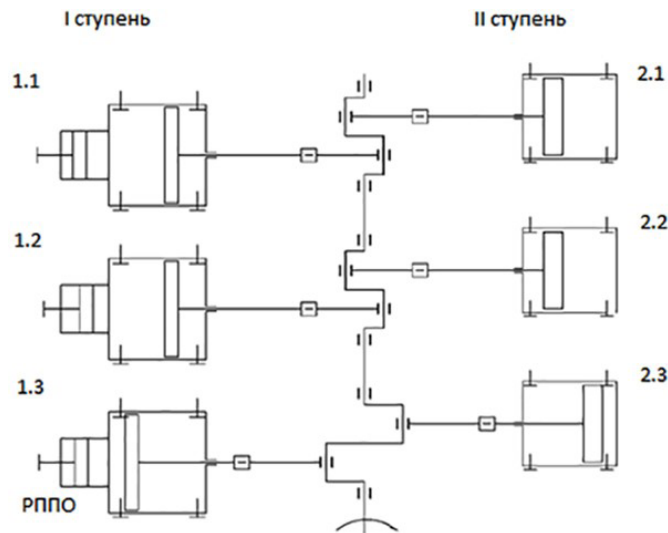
Схема оппозитного компрессора с обозначением цилиндров
